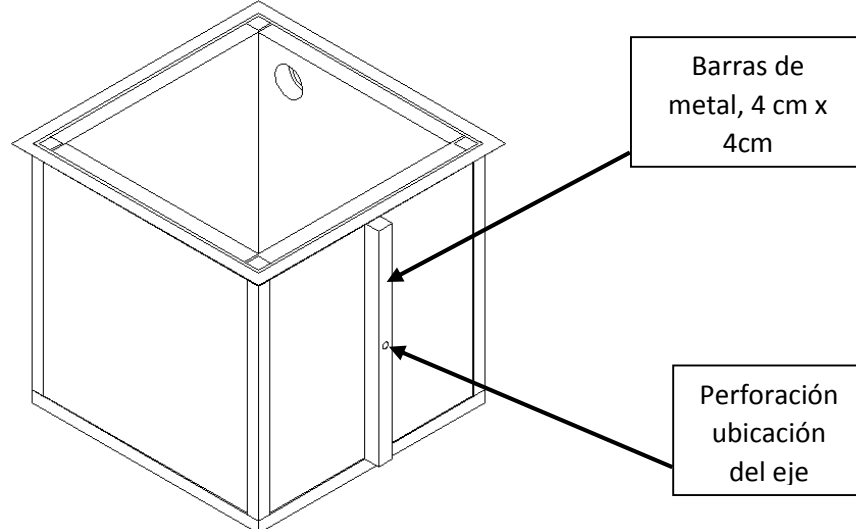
Isométrico barras soldados a los lados de la guarda unión del eje
